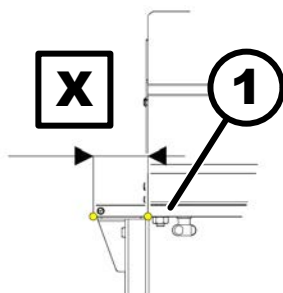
Dettaglio - Posizione di montaggio del braccio bandiera
